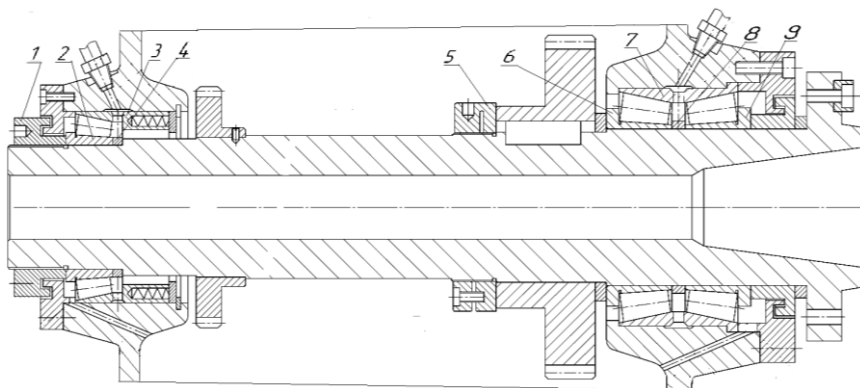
Шпиндельный узел с роликовыми радиально-упорными коническими двухрядным и однорядным подшипниками в опорах
